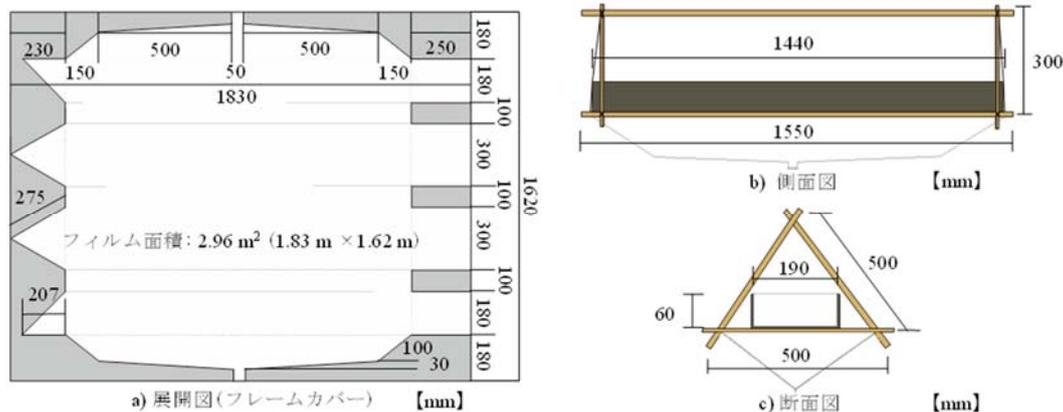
フレームカバーの展開図、TrSS の側面図および断面図
